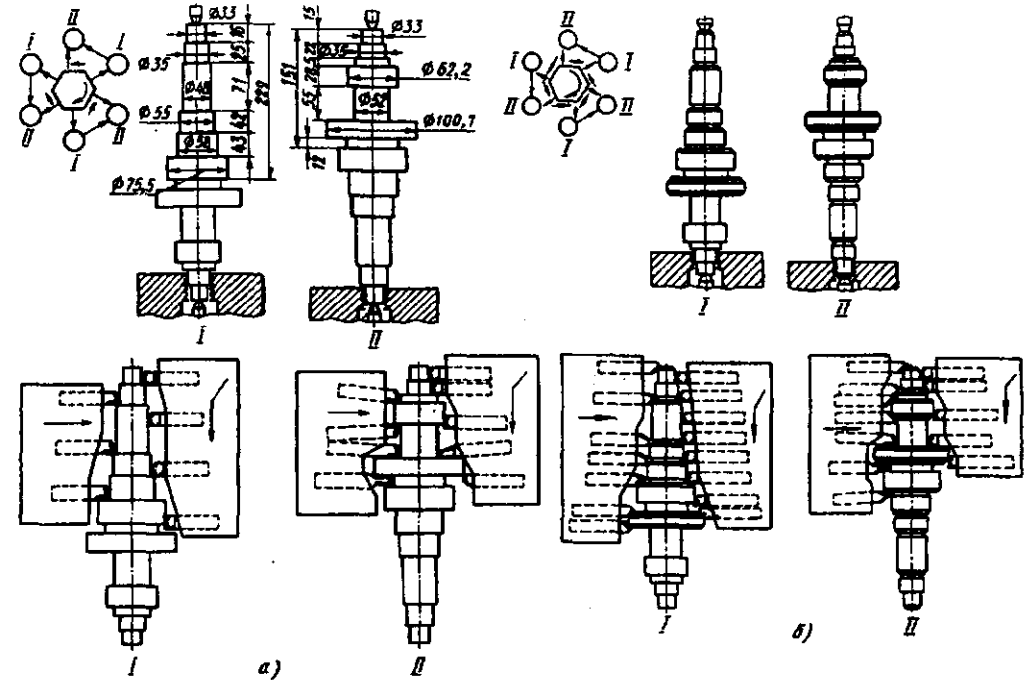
Наладки шестишпиндельного полуавтомата непрерывного действия для двухциклового обработки ступенчатого вала: а – черновой; б – чистовой
